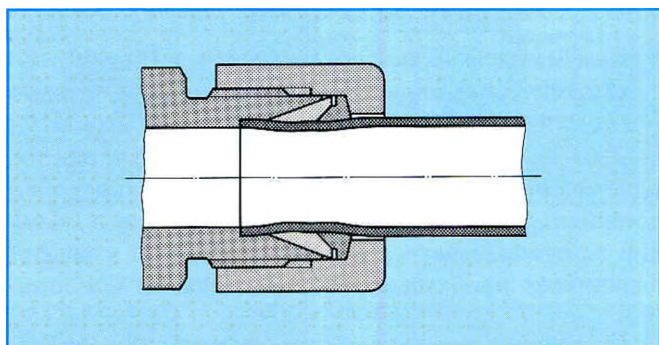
Резьбовое соединение с зажимным кольцом. Уплотнение: металл по металлу. Фиксация обеспечивается зажимом поверхности трубы.
